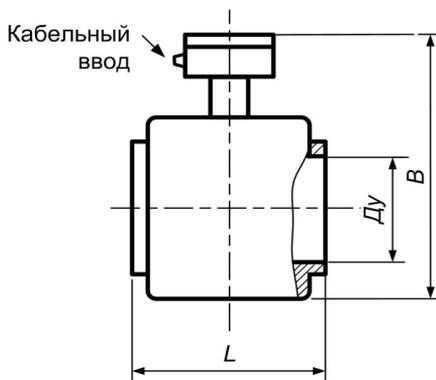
Конструкция сенсора без фланцев с монтажной коробкой
